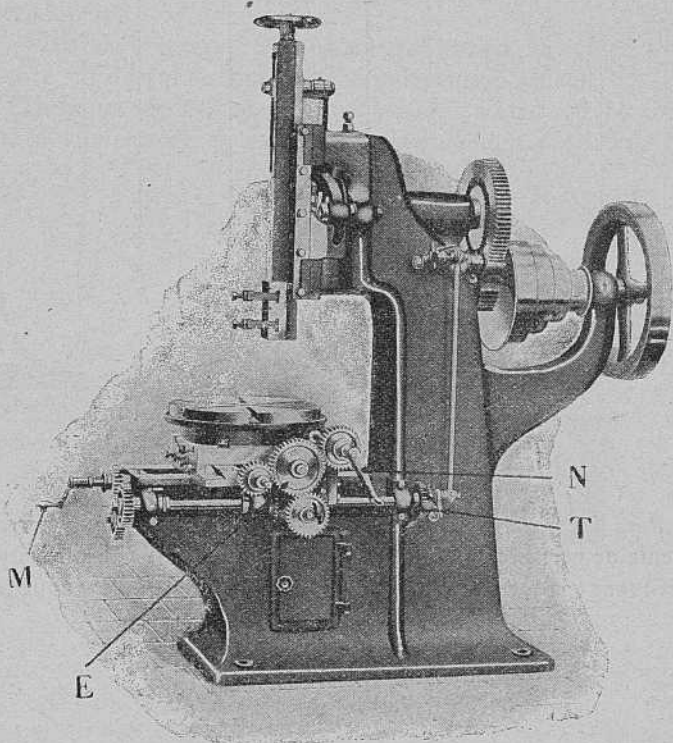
Mortajadora. *T*, trinquete; *N*, manivela para girar la mesa; *E*, combinación de engranajes para el movimiento automático de la mesa; *M*, manivela del carro.
